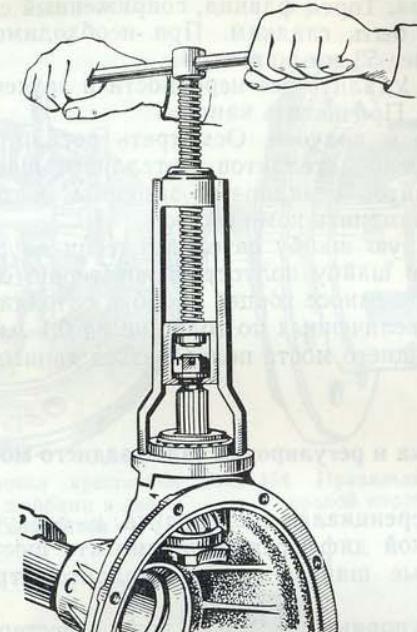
Снятие заднего подшипника с ведущей шестерни
